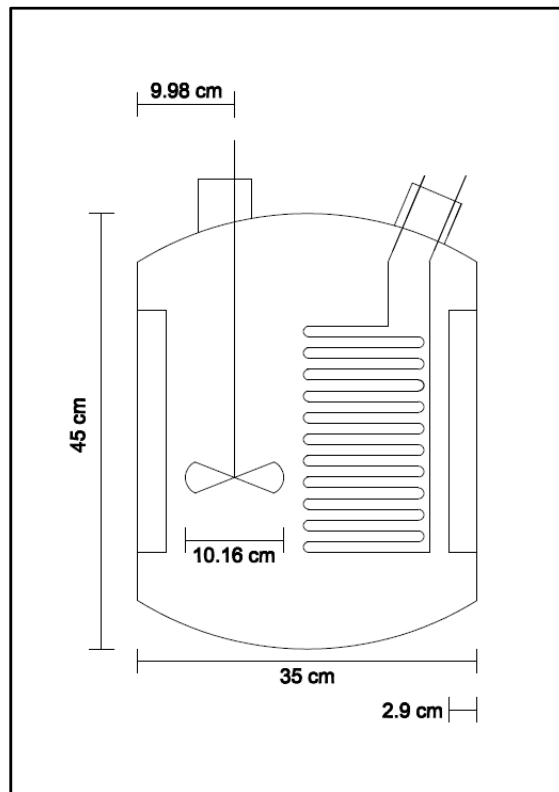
Dimensiones del reactor. El esquema incluye el serpentín a diseñar.
